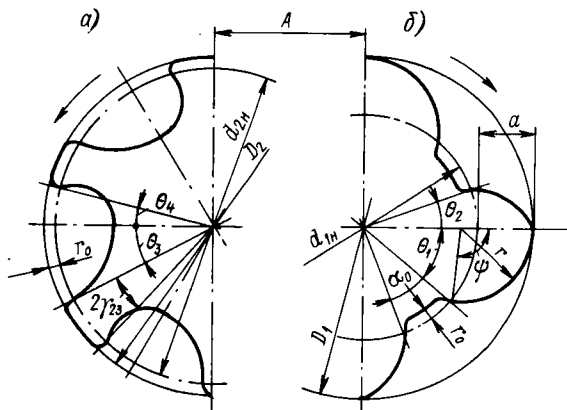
Торцевые сечения ВМ (а) и ВЦ (б) винтов типоразмерного ряда с зубом асимметричного профиля:
